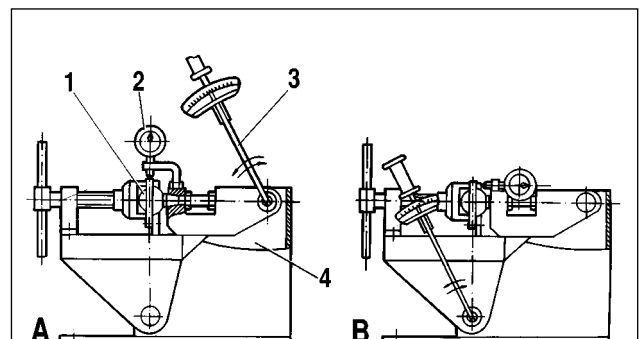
Kontrolle des Kugelgelenks mit Vorrichtung 02.8701.9502:
